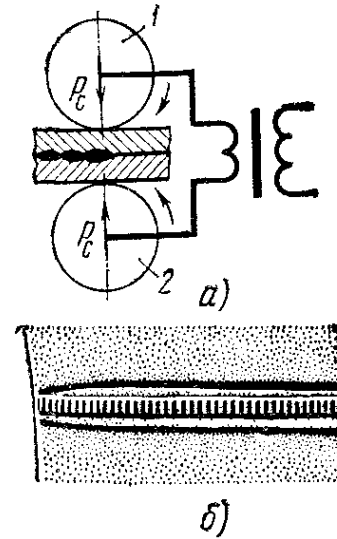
Схема шовной сварки (а) и сварной шов (б)
